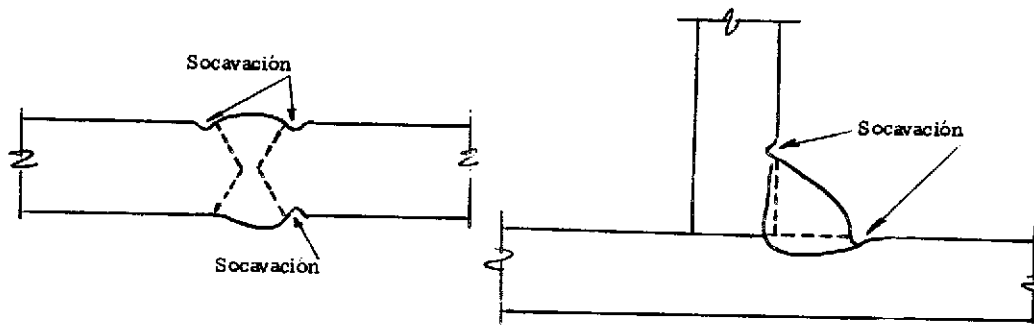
Socavación en soldadura de bisel y en soldadura de filete.
